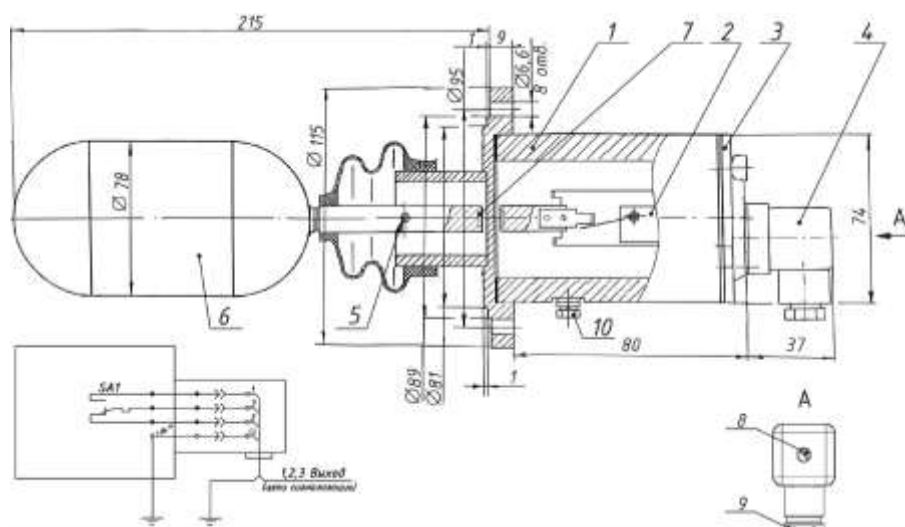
Габаритные и присоединительные размеры РОС 400-6
